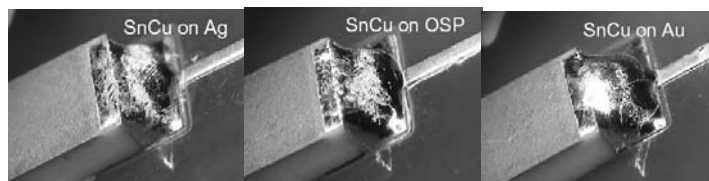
不同 PCB 表面保护层的无铅波峰焊焊点
